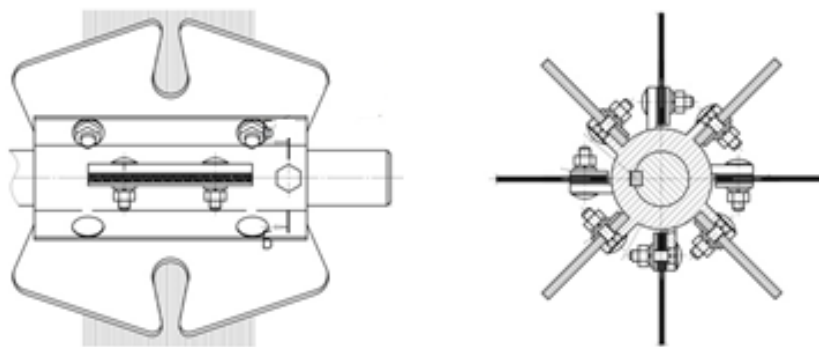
Лопатево-роторний притискний пристрій з розсічниками обгортки
